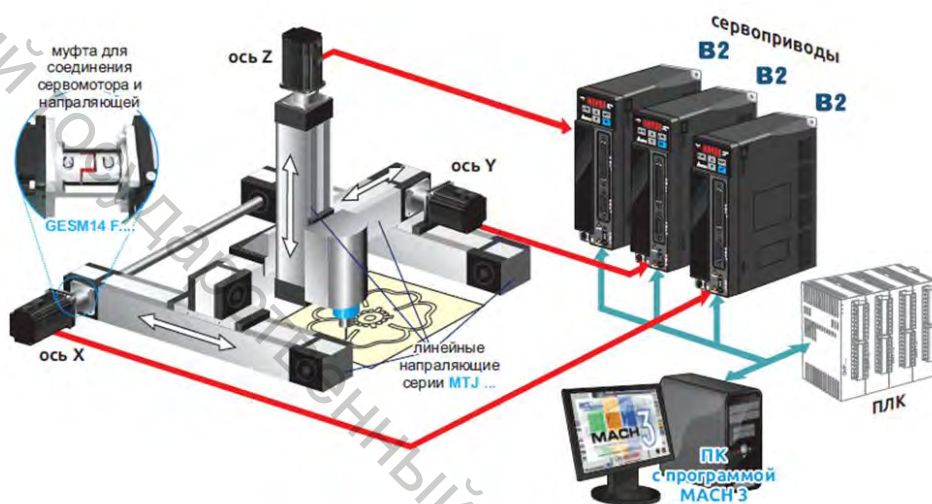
Основные элементы станка с ЧПУ фрезерной группы
